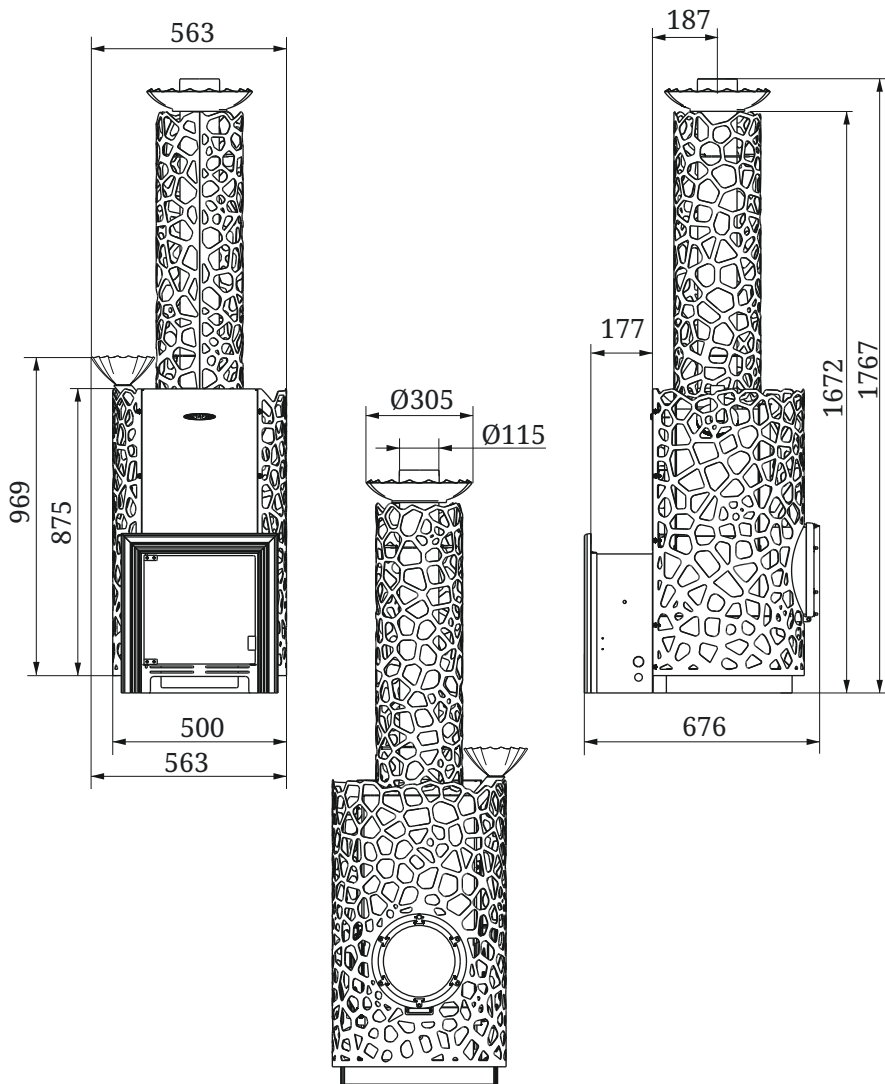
Габаритно-монтажные размеры печи «Аврора Газ»
